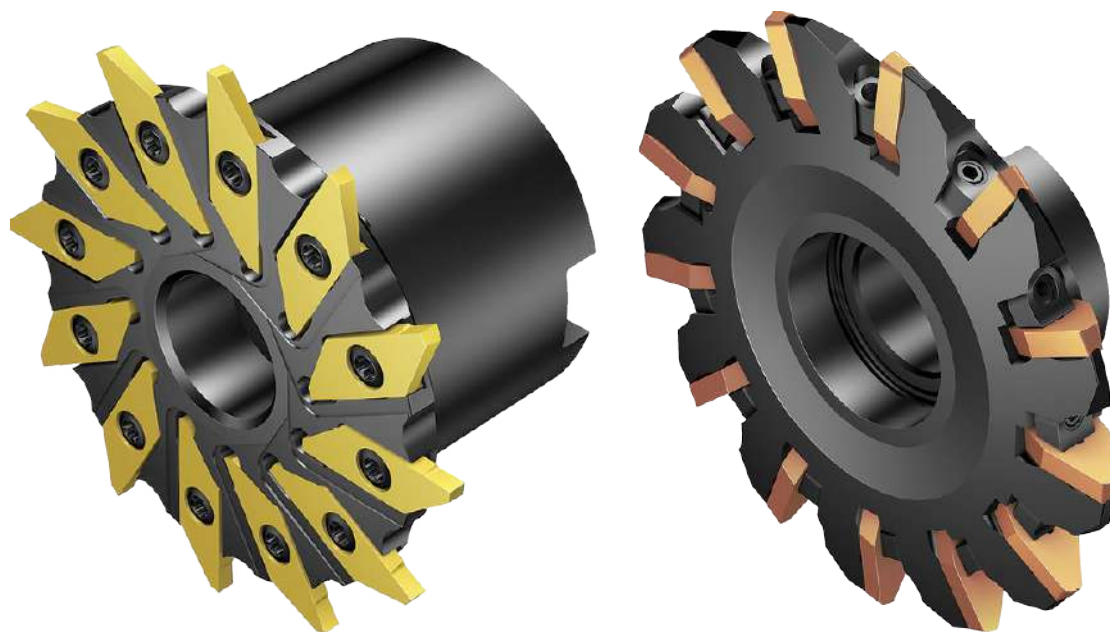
Фрези для нарізки зубів фірми Sandvick [7]
